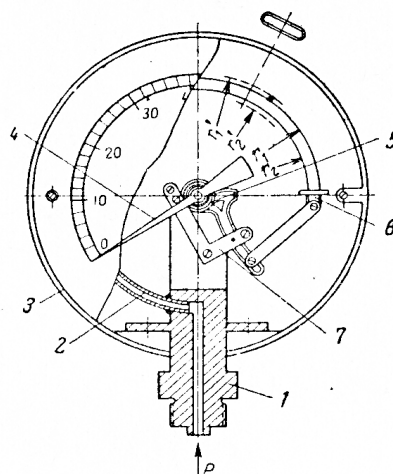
Манометр с одновитковой трубчатой пружиной:
